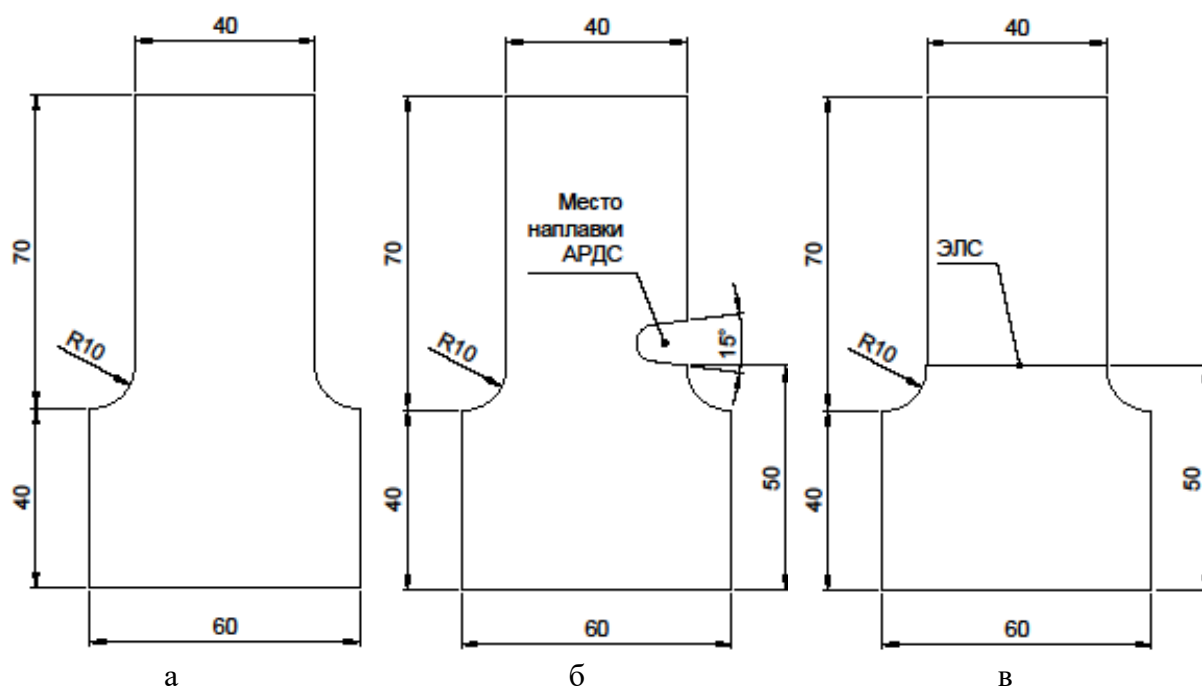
Образцы для испытаний: а) контрольный образец; б) образец с наплавляемым АрДС соединением; в) образец с соединением ЭЛС
